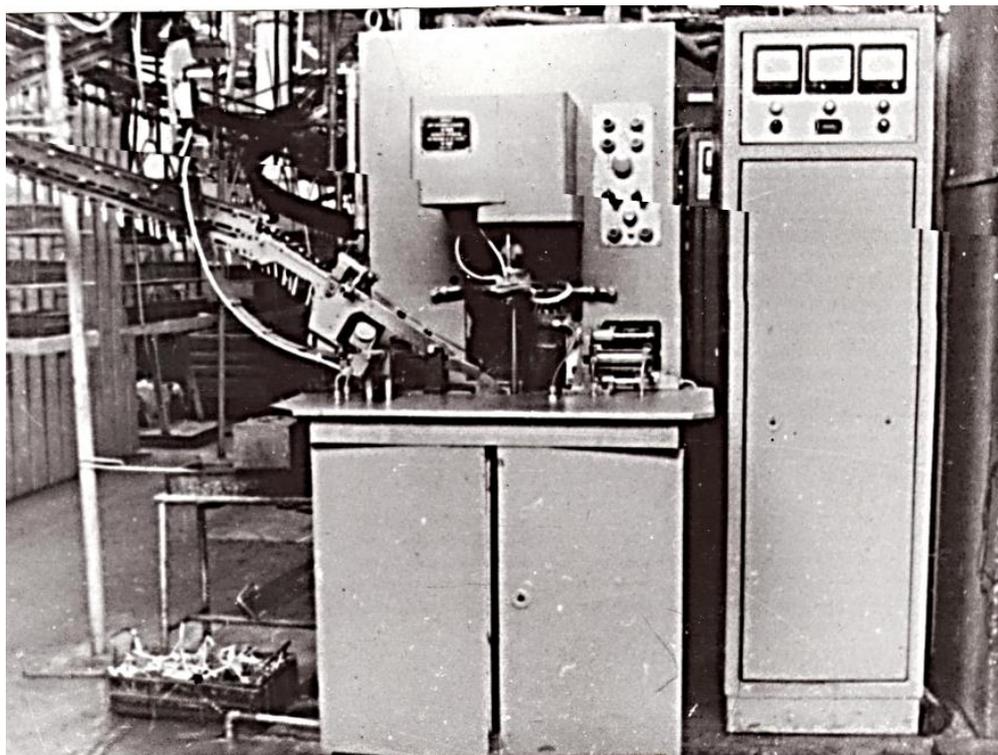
Установка для наплавлення типу ОБІ099М
